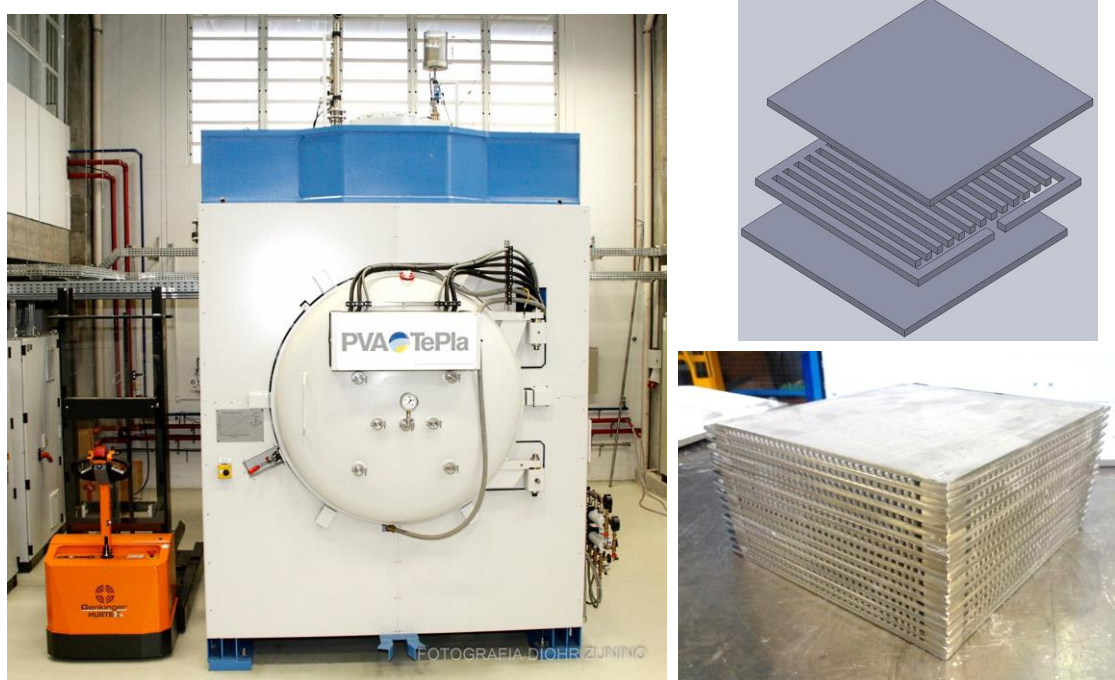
Forno de soldagem por difusão e peças produzidas no forno.
